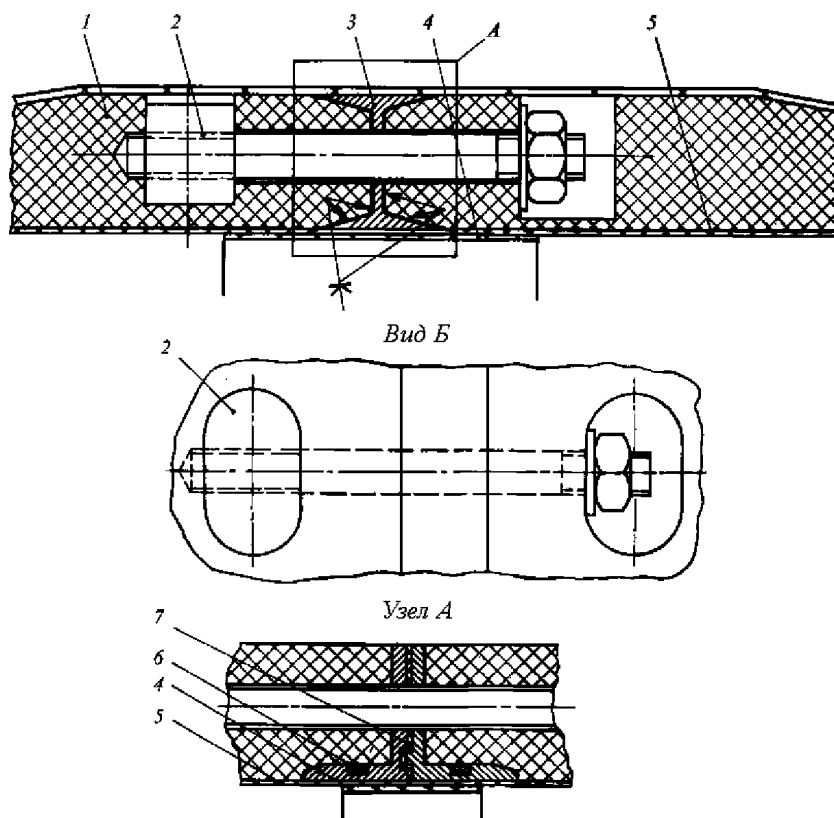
Конструктивное оформление шпильочно-штифтовых соединений элементов силовой оболочки цистерны:
